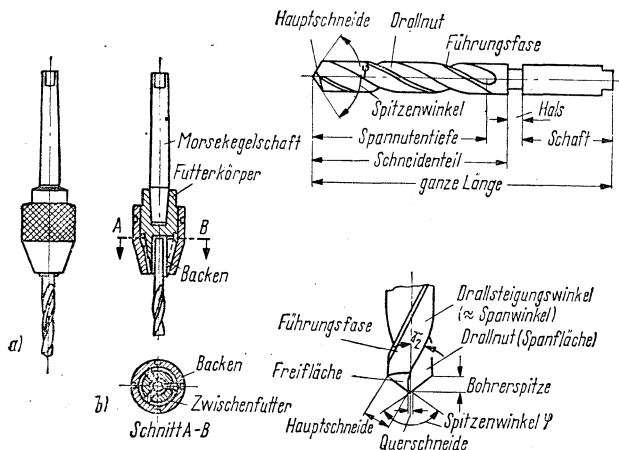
Bohrwerkzeuge; links Dreibacken-Bohrfutter mit konischem Schaft, rechts oben Spiralbohrer mit Bezeichnung der Einzelheiten und rechts unten die Bohrerspitze mit den entsprechenden Winkeln
